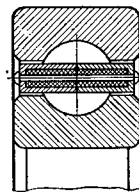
Шарикоподшипник, в сепаратор которого запрессован твердый смазочный материал
